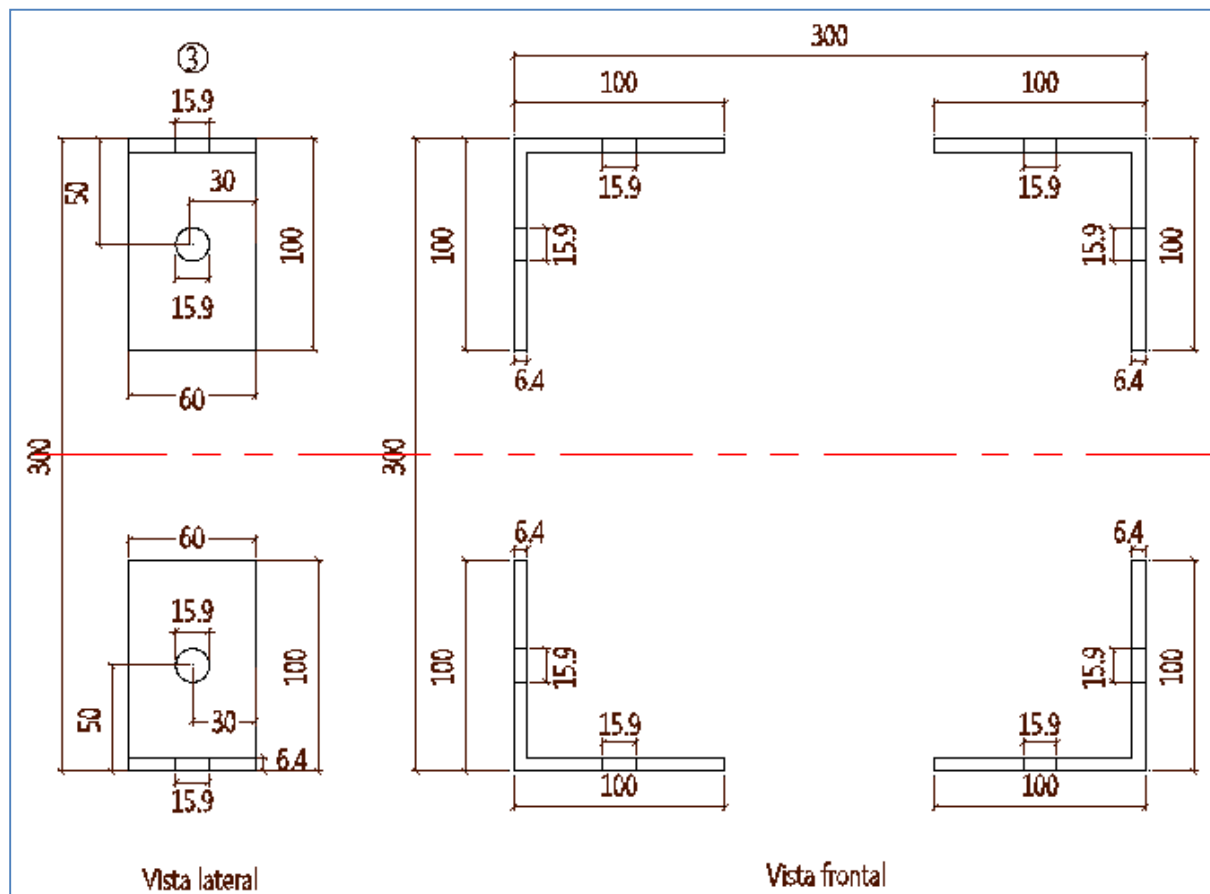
Detalle despiece pieza No.3 modelo 1 flexión.
